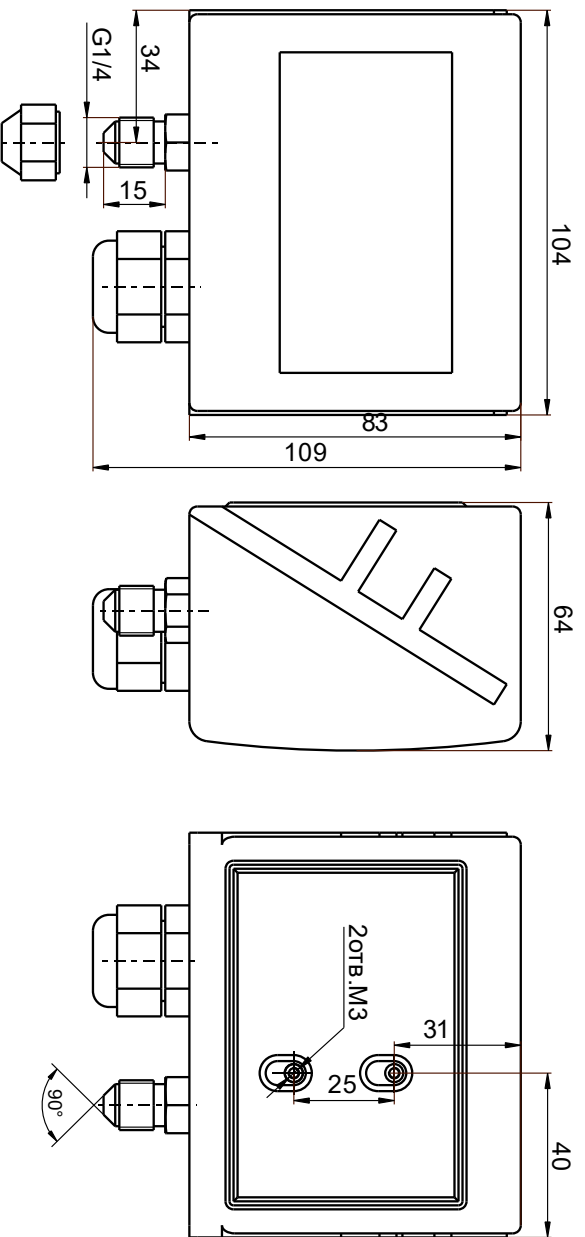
Габаритные и присоединительные размеры РД-2Р в корпусе IP55
